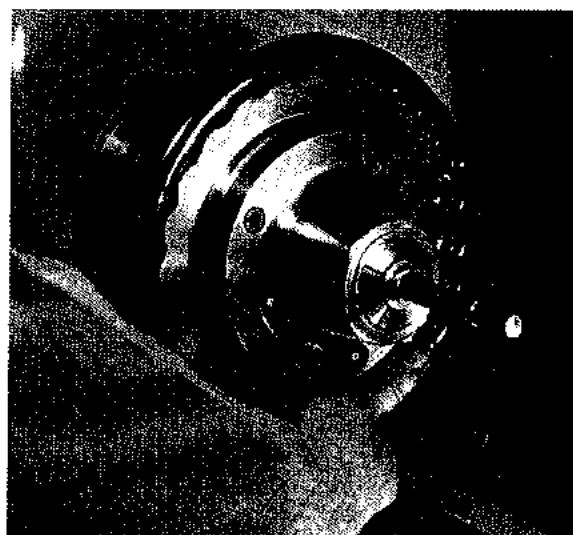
Plato con casquillo elástico, tipo Sjogren, montado en el extremo del husillo (Cincinnati Lathe & Tool Co.).
